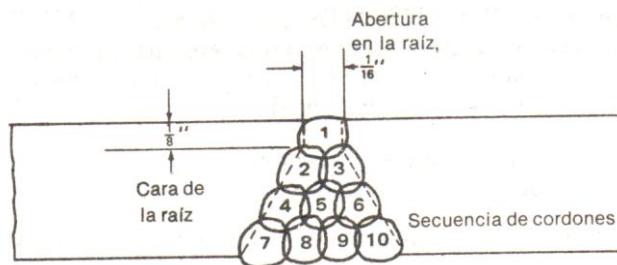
Secuencia de la aplicación de los cordones de soldadura.
